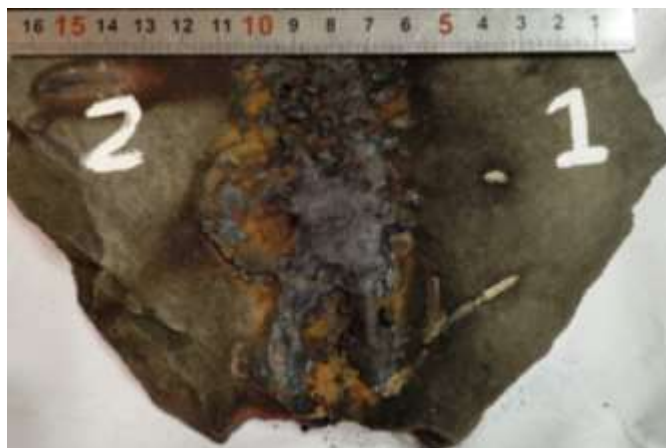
Сварной шов, образованный на месте стыка образцов
